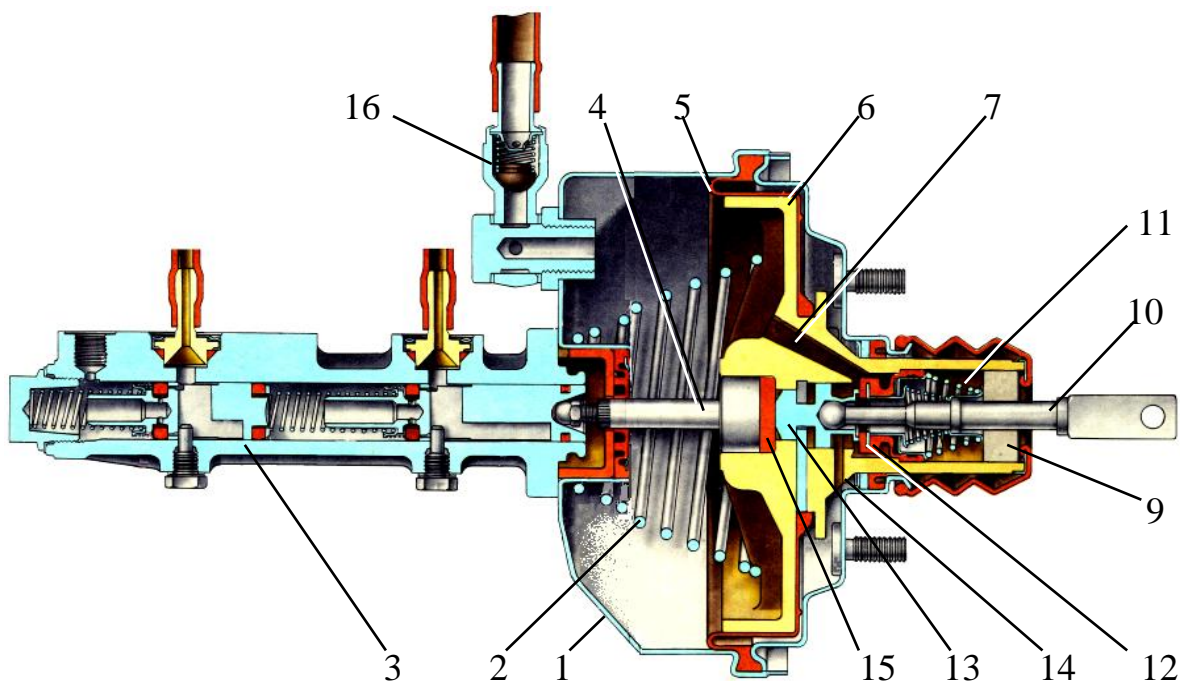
Конструкция вакуумного усилителя гидравлического тормозного привода: 1 – корпус усилителя; 2 – пружина; 3 – главный тормозной цилиндр; 4 – шток; 5 – диафрагма; 6 – поршень усилителя; 7 и 14 – каналы; 9 – фильтр; 10 – шток педали; 11 – пружина вакуумного клапана; 12 – вакуумный клапан; 13 – плунжер; 15 – упругая шайба; 16 – запорный клапан
